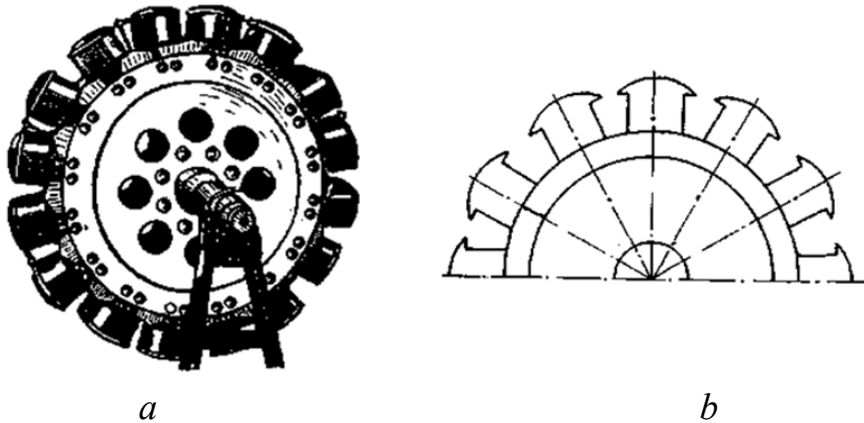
Rotor d'une machine synchrone à pôles saillants :
